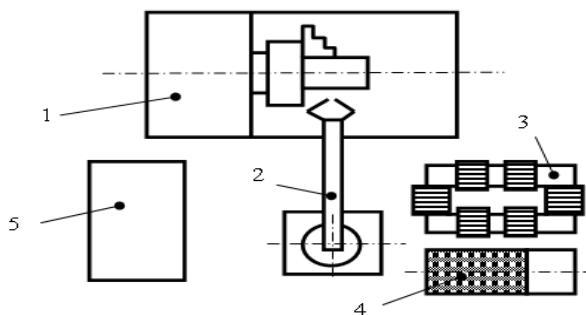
Схема ГПМ на базе токарного обрабатывающего центра:
